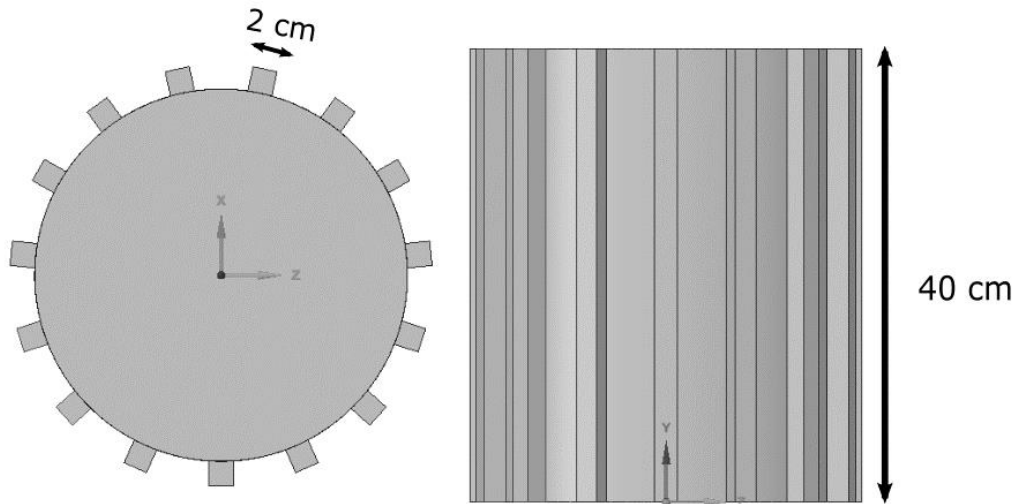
Vista lateral y superior de herramienta de corte para tubería central (Fuente: Gil, 2020)
